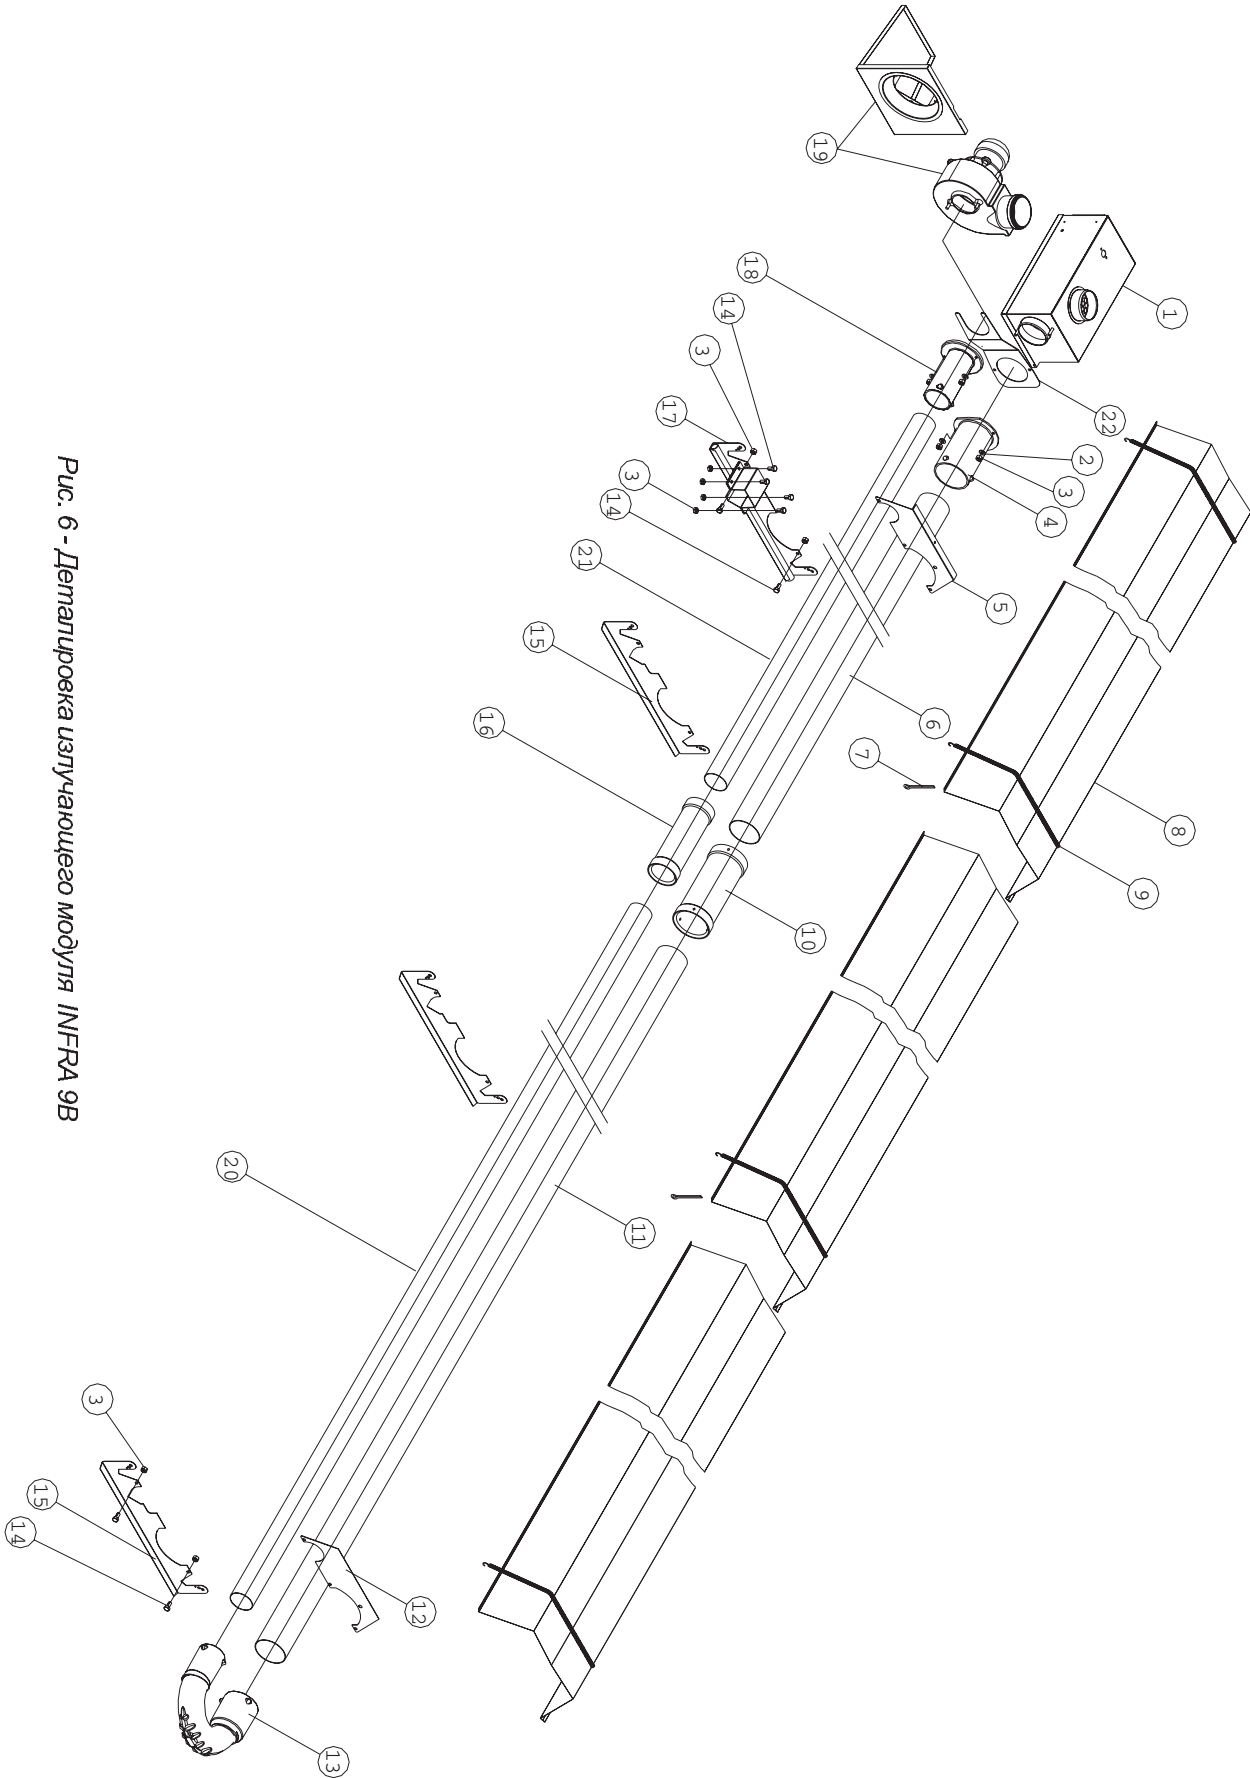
Детализировка излучающего модуля INFRA 9B
